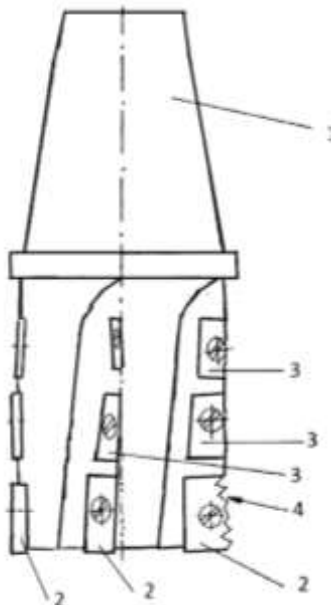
Концевая фреза с механическим креплением режущих пластин.
